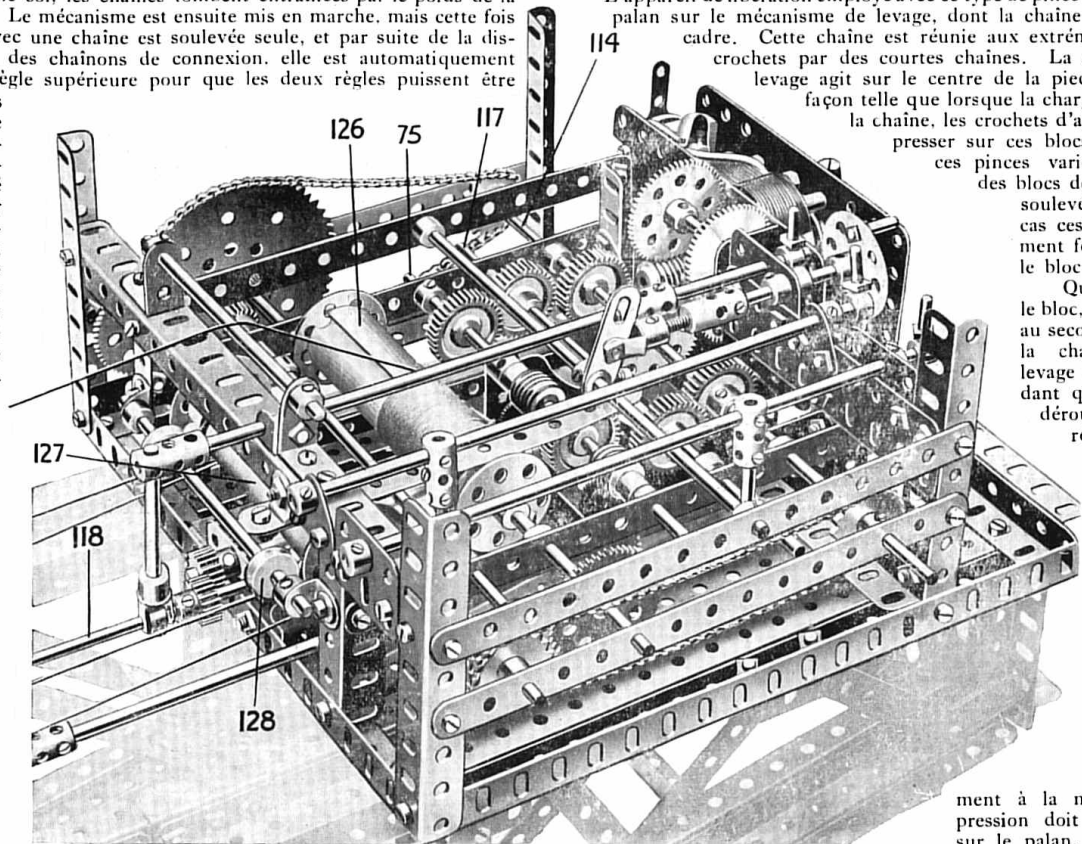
Vue générale de la Boîte à Engrenages avec tout son mécanisme monté
